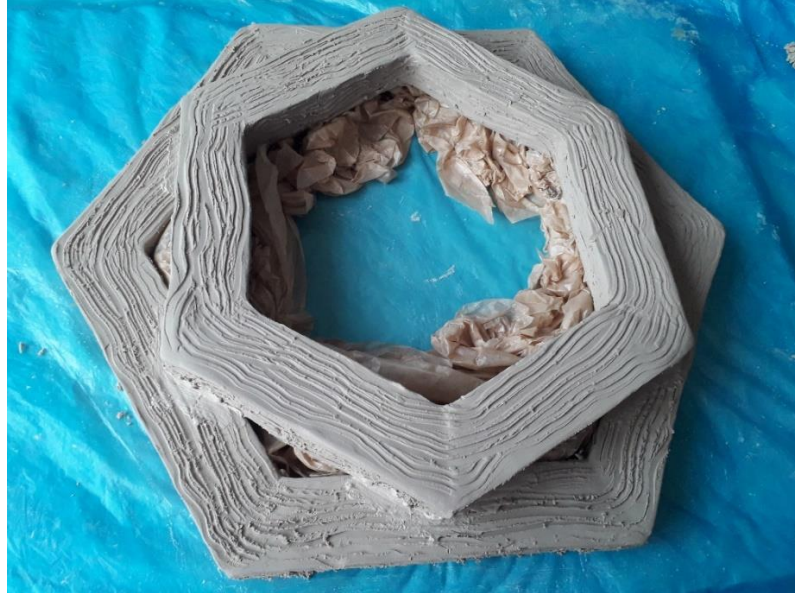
Fırın Sonrası Arka Plandan Detay
